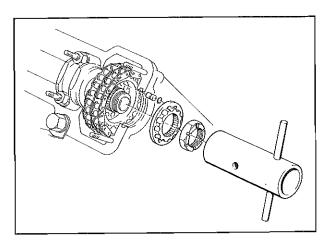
Allentare i dadi di bioccaggio Slacken locking nuts
